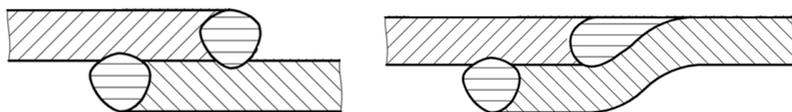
Схемы нахлесточных сварных соединений
